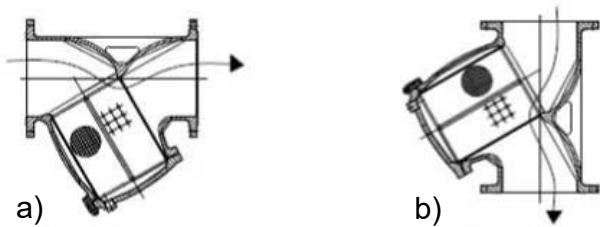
a) Horizontaler Einbau / b) Vertikaler Einbau
